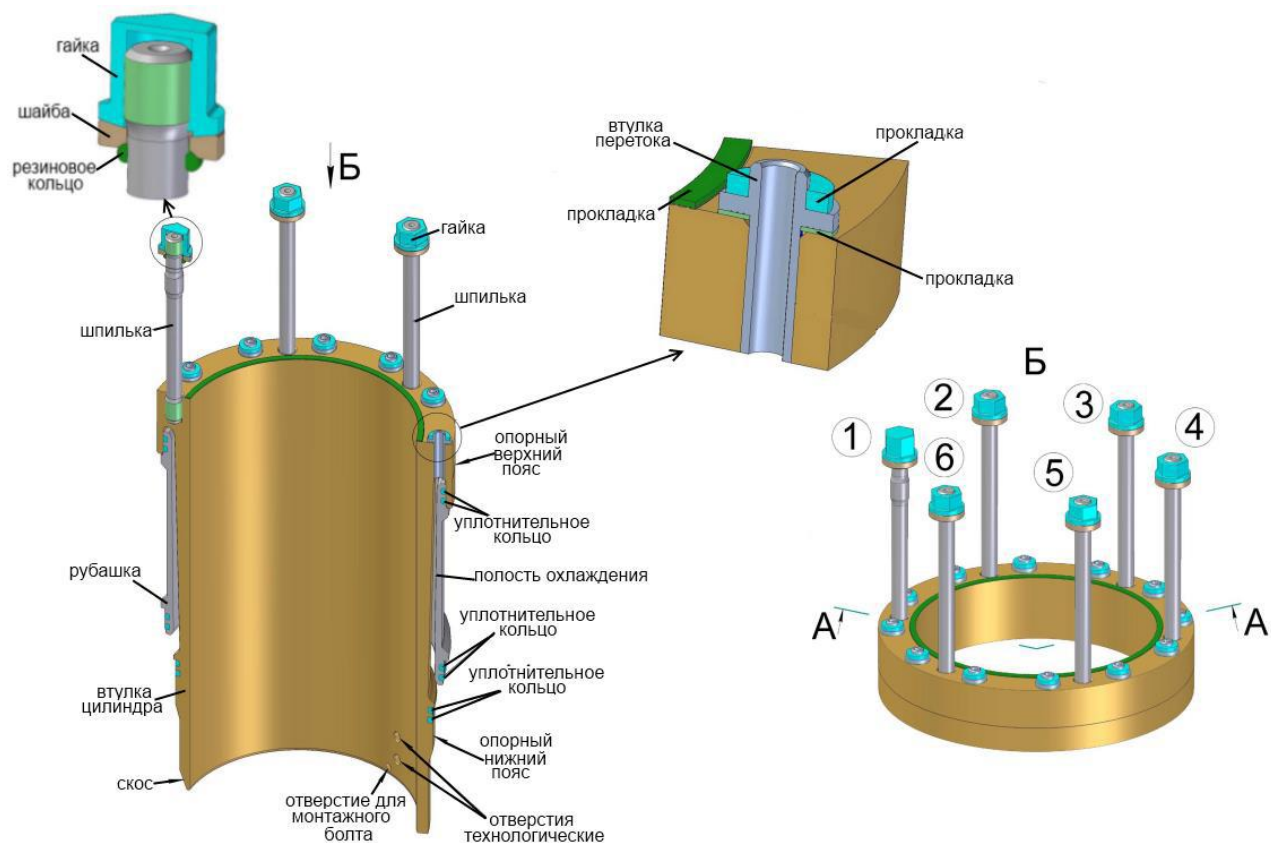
Цилиндровая втулка. Цифры в кружках, порядок затяжки гаек
